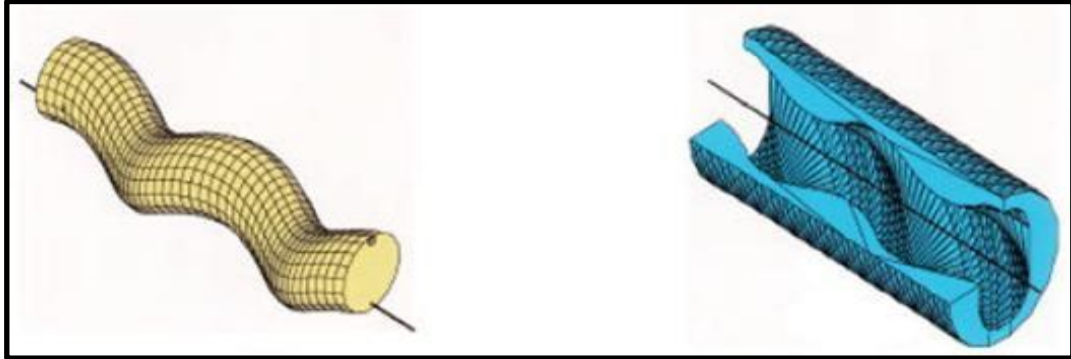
Diseño de Rotor y Estator Helicoidal ESPCP
